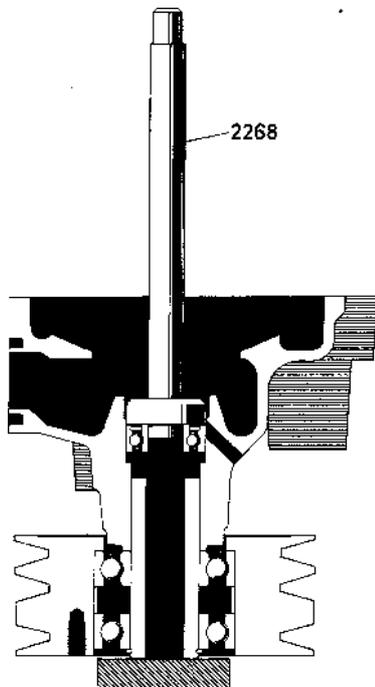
Remontage du roulement arrière dans le corps de pompe
